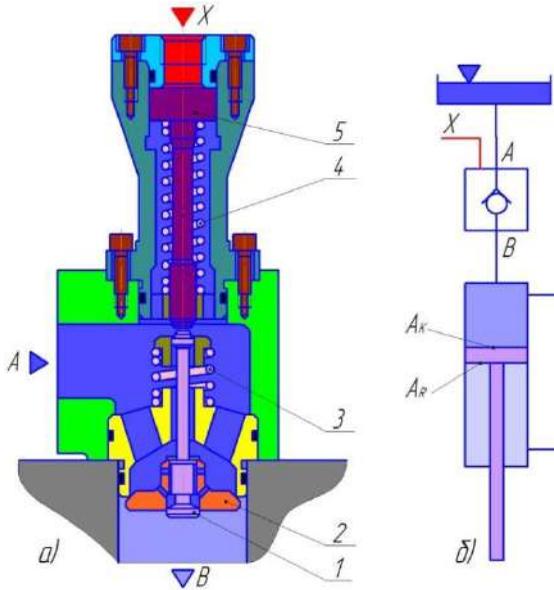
Клапан наповнення з декомпресором:
